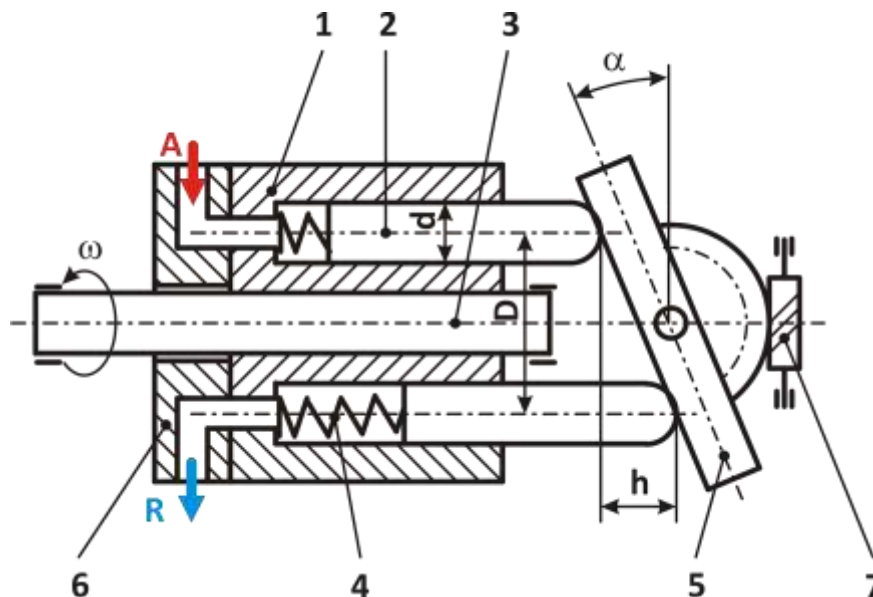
Pompa cu pistonășe axiale cu disc înclinat
